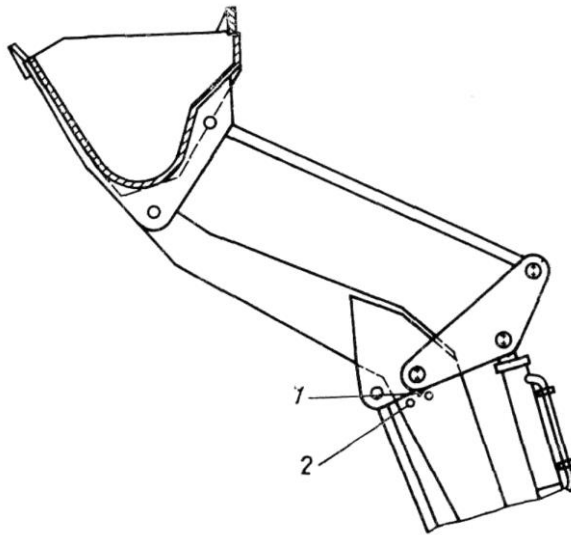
Показчик положення ковша: 1 – стрілка; 2 – бонка
